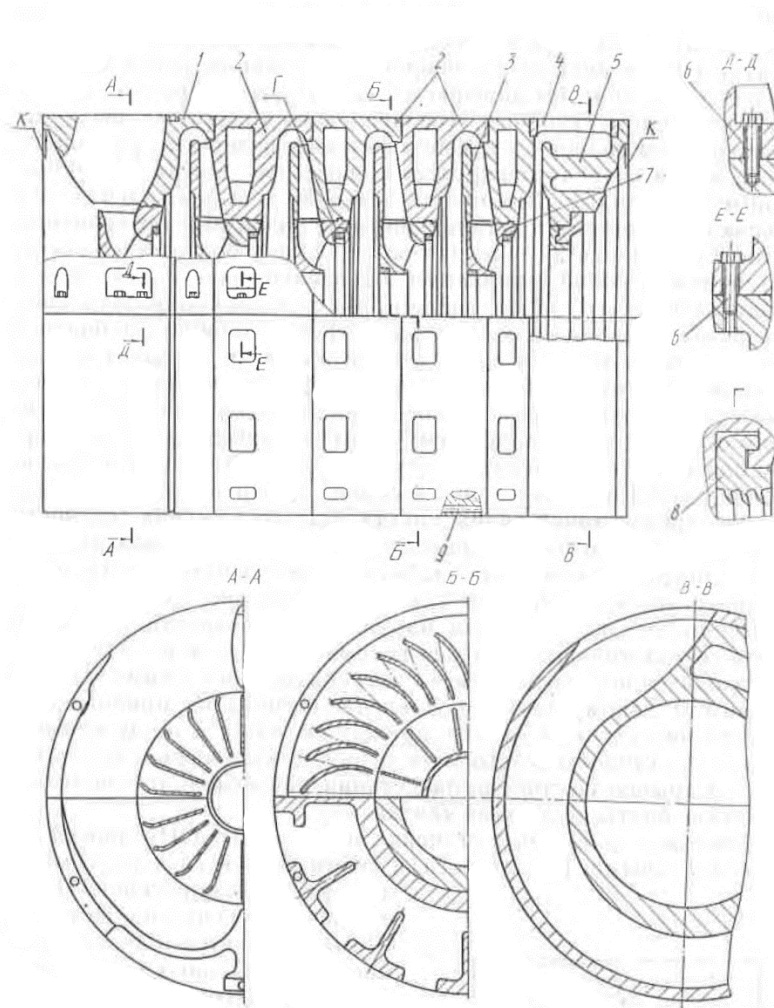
Комплект диафрагм компрессора с вертикальным разъемом. 1 – всасывающая камера; 2 – промежуточная диафрагма; 3 – внутренняя перегородка с ОНА; 4 – распорное кольцо; 5 – концевая диафрагма с улиткой; 6 – болты, сваривающие половинки диафрагм; 7 – лопаточный аппарат; 8 – лабиринтная втулка; 9 – стяжные шпильки
